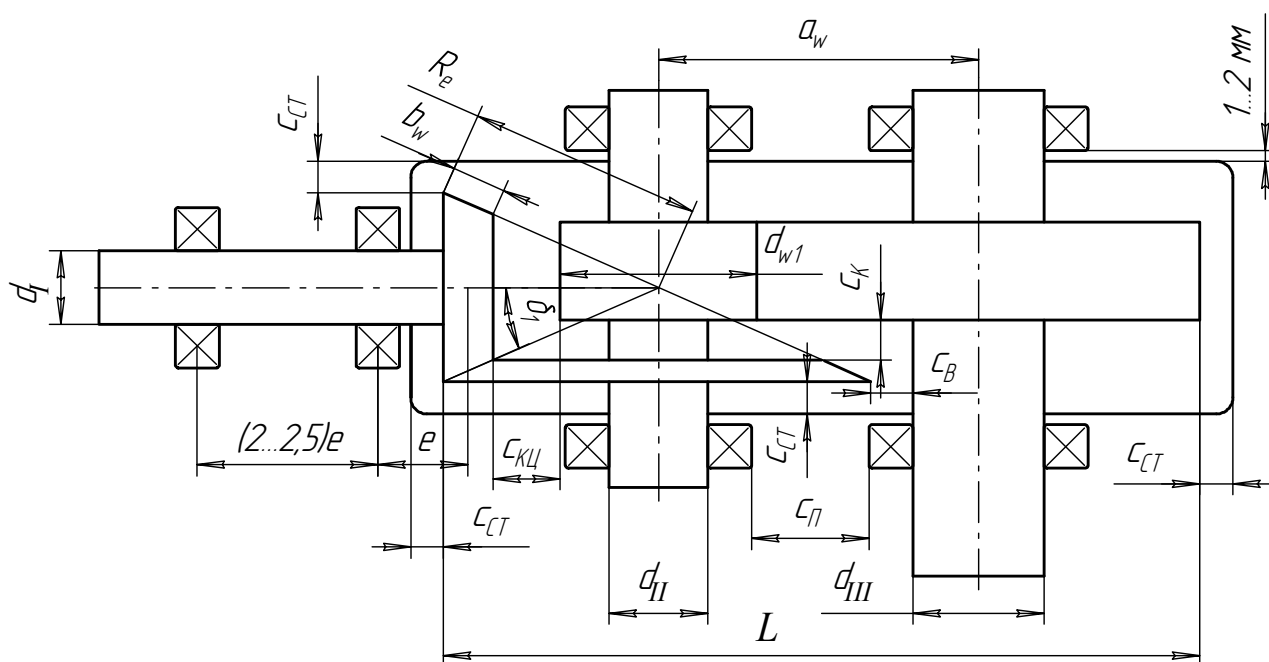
Расположение колёс и подшипников коническо-цилиндрического редуктора
